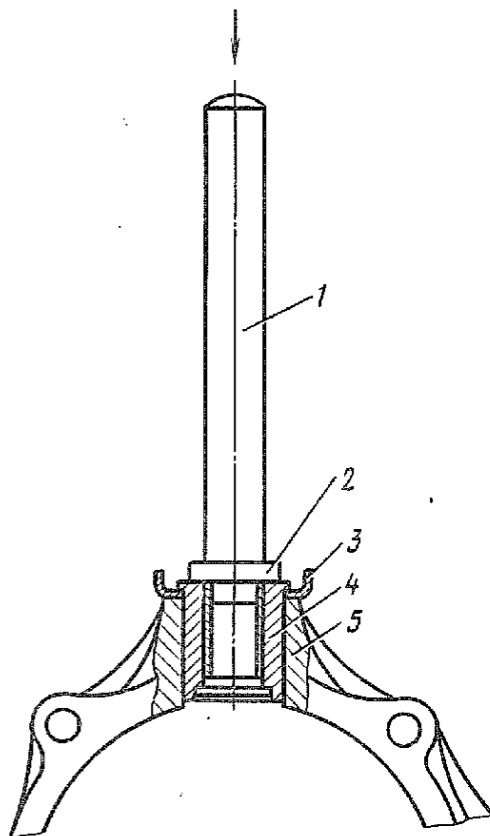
Запрессовка корпуса втулки с втулкой в сборе в поворотный кулак:
